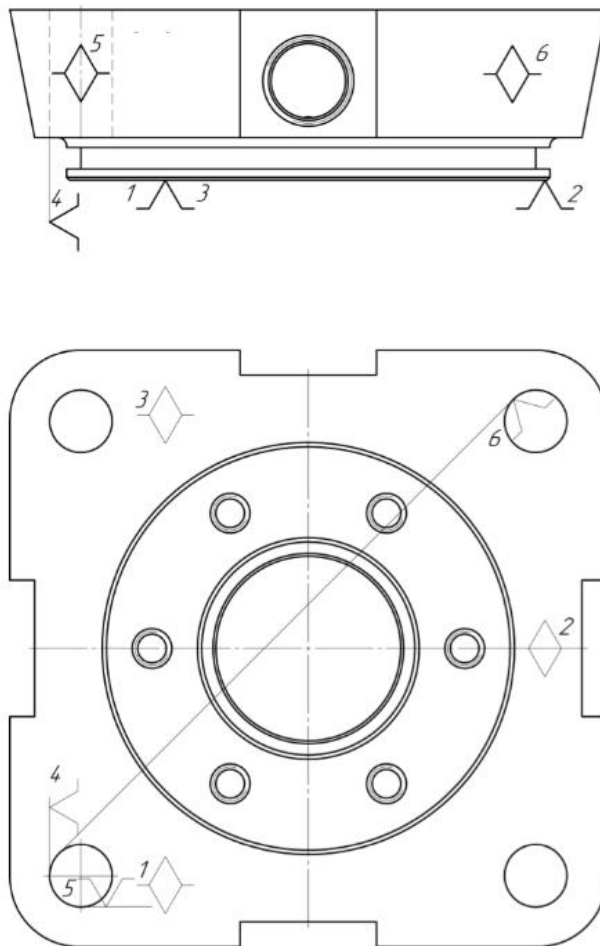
Схема базування деталі «Корпус» по ЗТБ 1.
